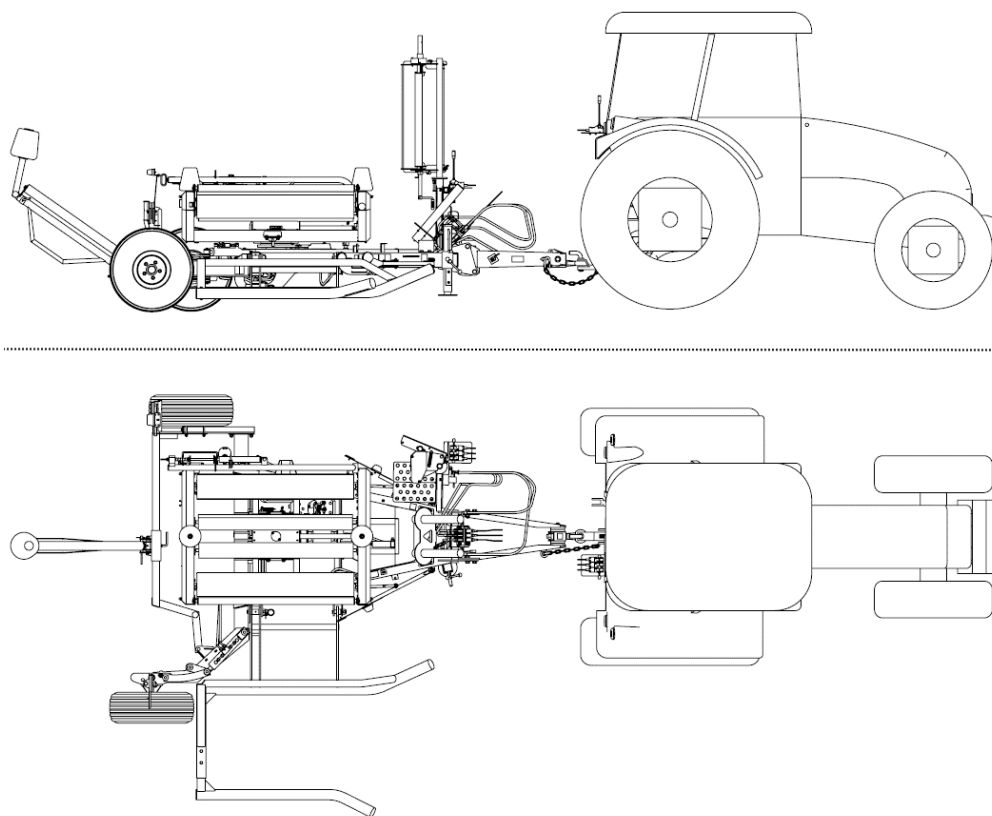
Blokada pozycji ramienia załadowczego: A – pozycja transportowa ,
